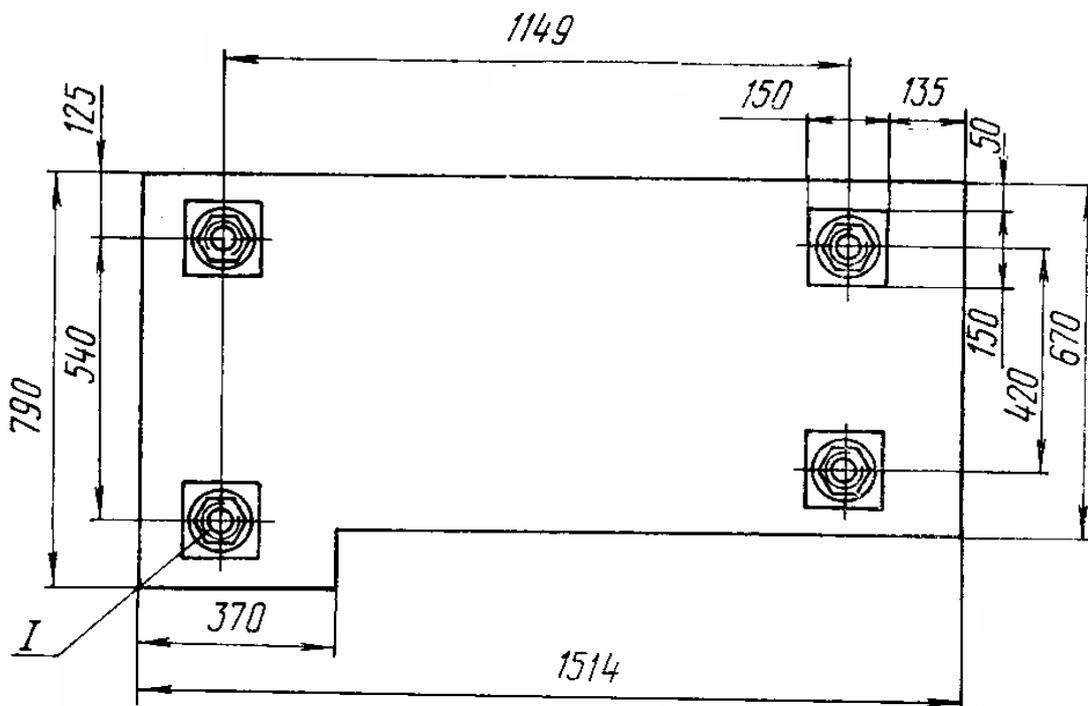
Схема установки пресс-ножниц НГ5223 на фундамент:
